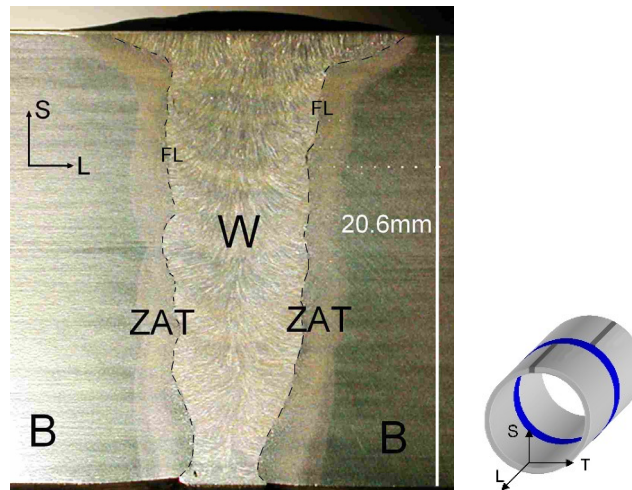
Coupe macroscopique de la soudure de rabouillage (2B50)
